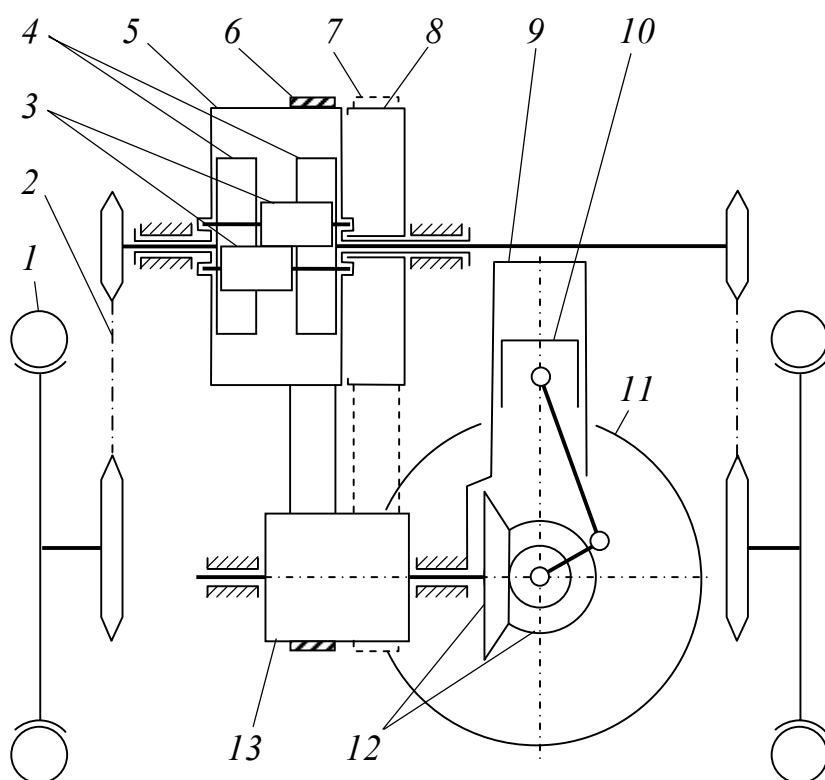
Трансмиссия автомобиля Бенца, 1885 г.: 1 – ведущее колесо автомобиля; 2 – цепь привода колеса; 3 – сдвоенные сателлиты; 4 – полуосевые шестерни; 5 – ведомый шкив ремённой передачи; 6 – ремень в положении «движение»; 7 – ремень в положении «холостой ход»; 8 – шкив холостого хода; 9 – цилиндр; 10 – поршень; 11 – маховик; 12 – коническая передача; 13 – ведущий шкив;
